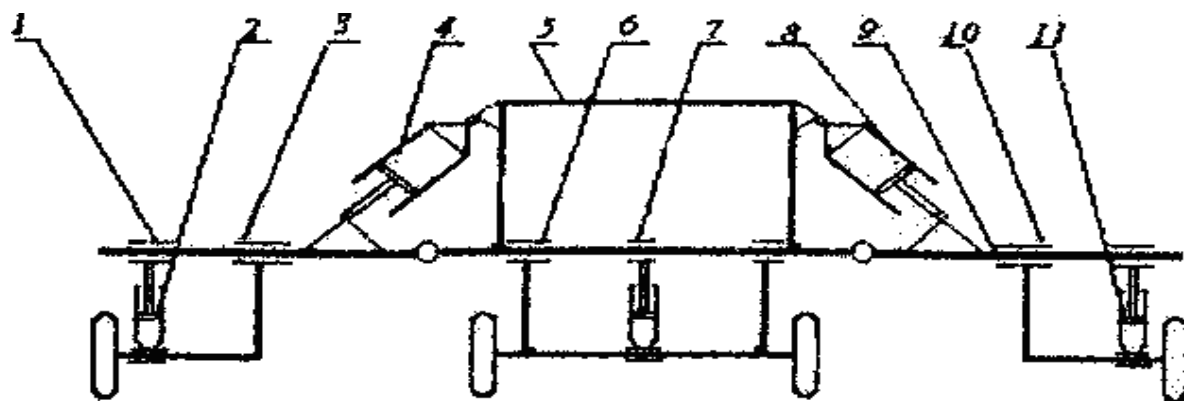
Культиватор для предпосевной обработки КПЗ-9,7: 1,9 - боковые секции; 2,7,11 - гидроцилиндры выглубления рабочих органов; 3Д10-механизм подката колес (выглубления рабочих органов); 4,8-гидроцилиндр сворачивания секций; 5- центральная секция культиватора
